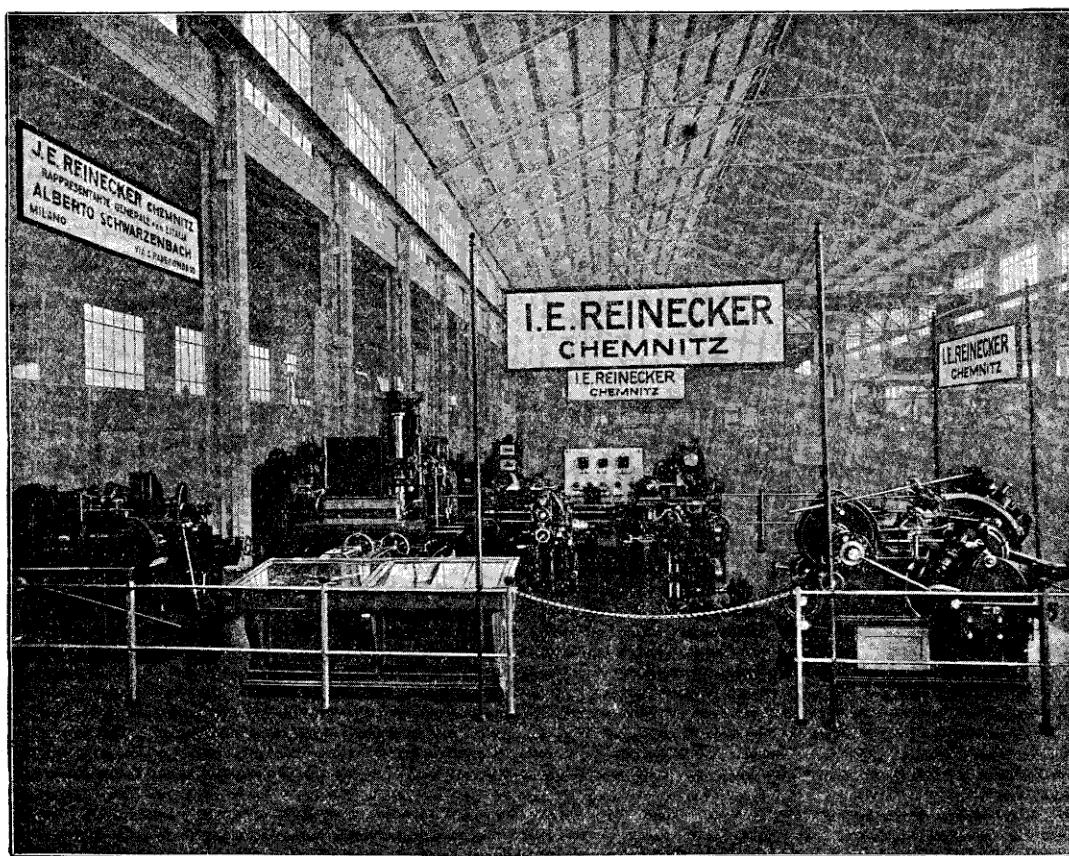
Vue du stand des Etablissements J.-E. Reinecker, de Chemnitz.
